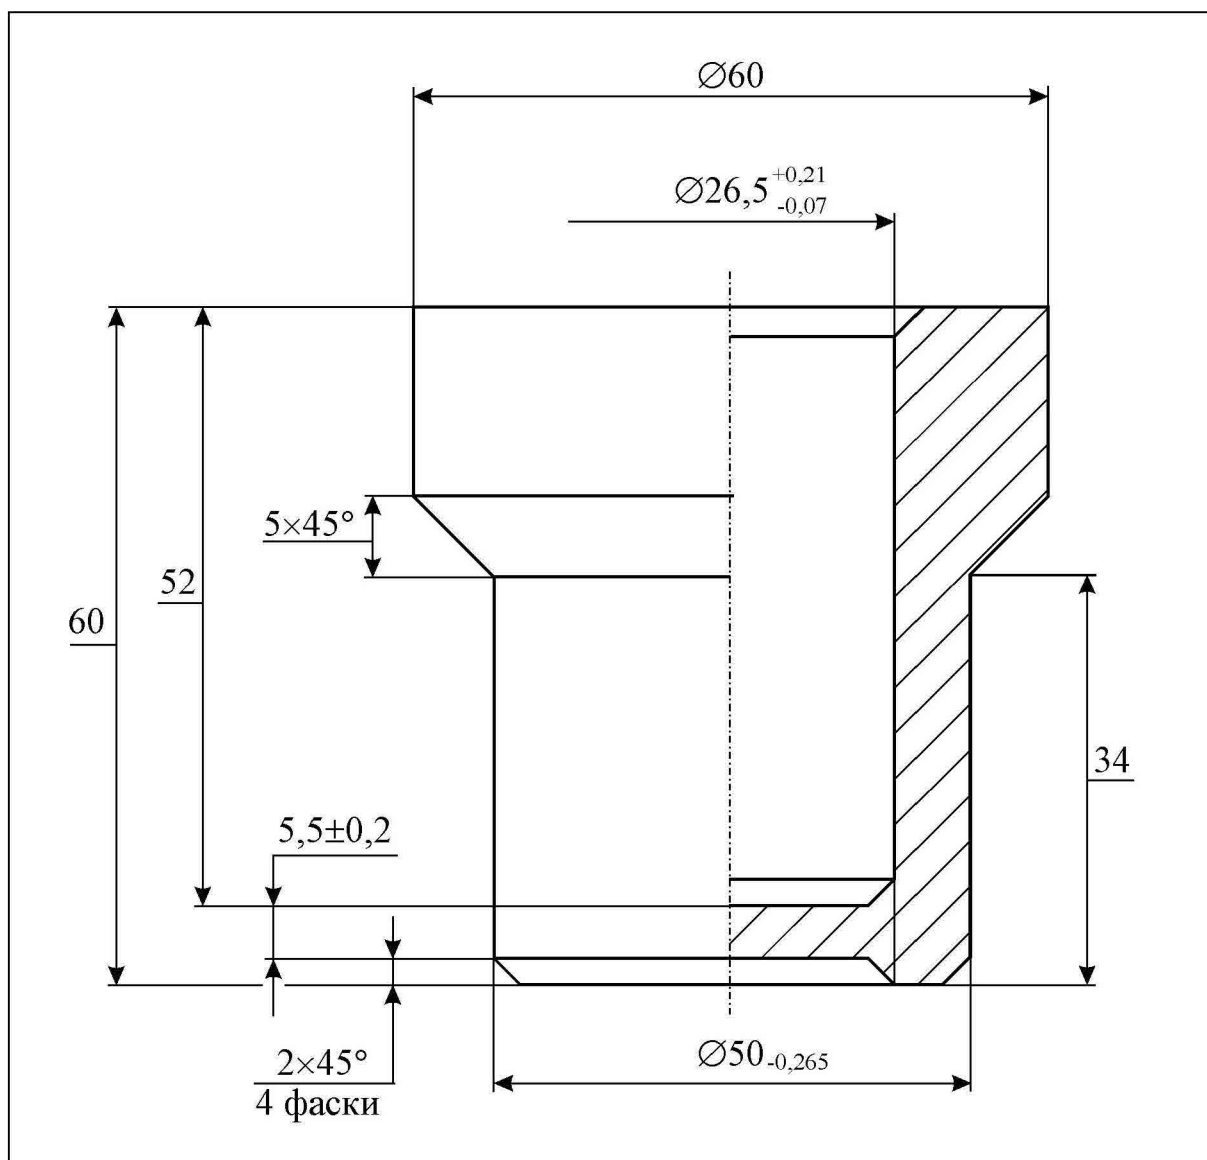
Кресленник деталі «Втулка» після холодного штампування перед подальшою механічною обробкою
